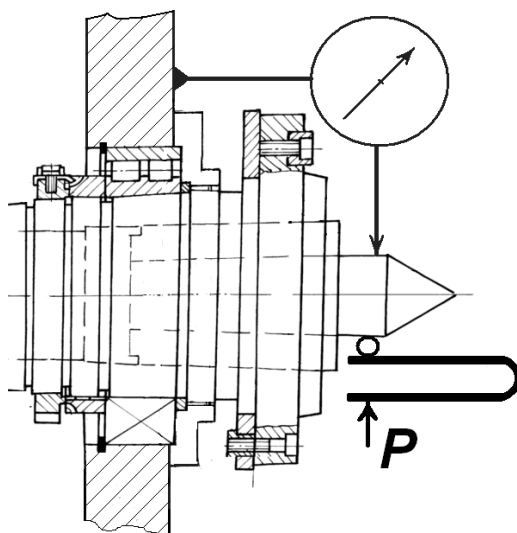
Нагружение шпинделя токарного станка 1М63Н-5
